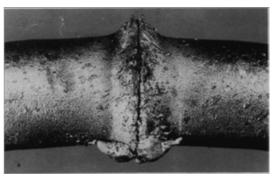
Stauchgrat einer Abbrennstumpfschweißung an einem Ketten-
